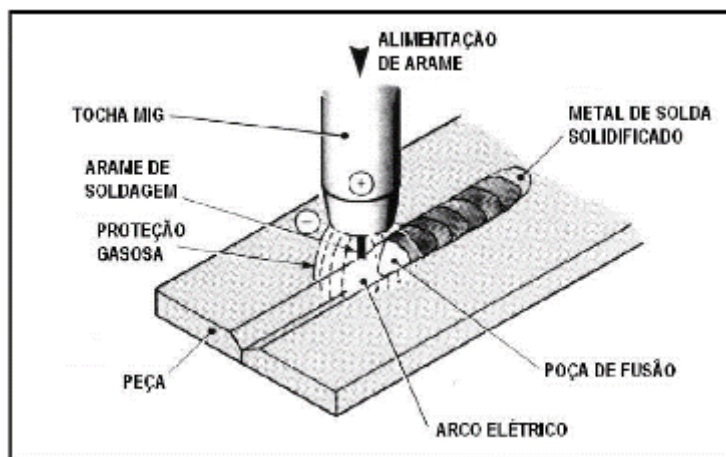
Processo básico de soldagem MIG/MAG <sup>(2)</sup>.
